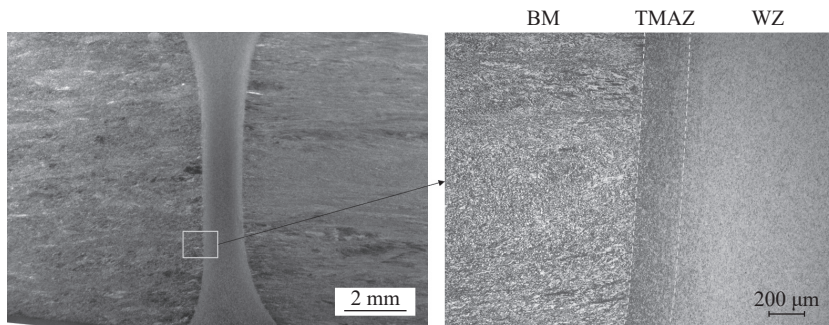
TA18 管摩擦焊接接头横截面形貌
